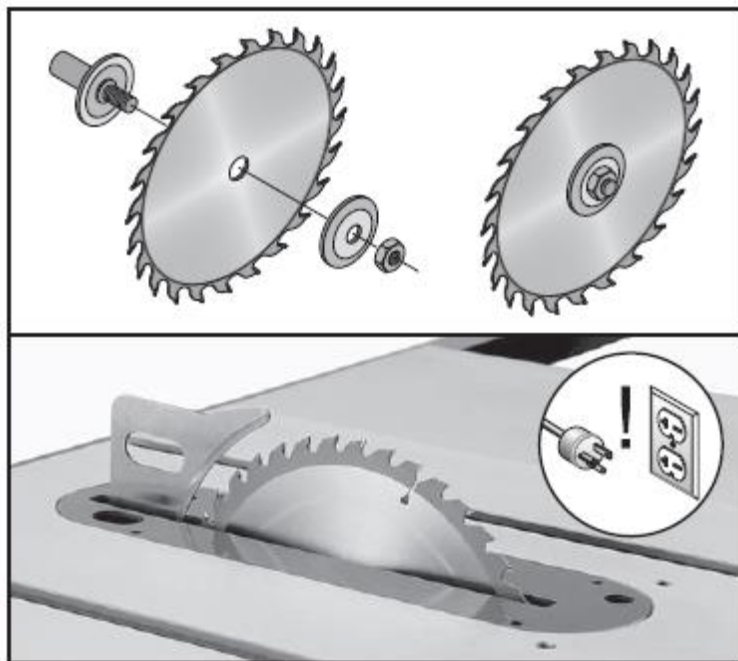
Порядок установки дисковой пилы и зубья в правильном направлении
